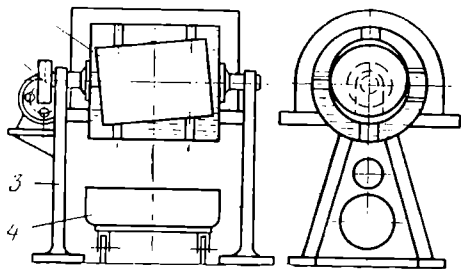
Бесшумный галтовочный барабан: 1 — барабан, 2 — редуктор, 3 — станина, 4 — тара
